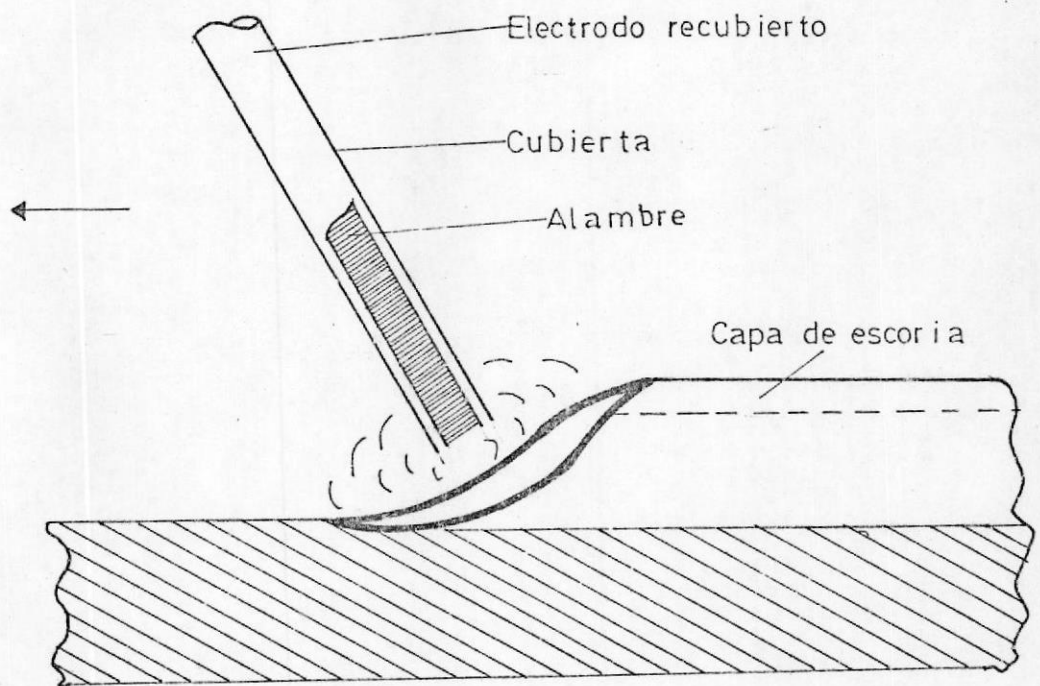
SOLDADURA POR ARCO CON ELECTRODO REVESTIDO (6)
